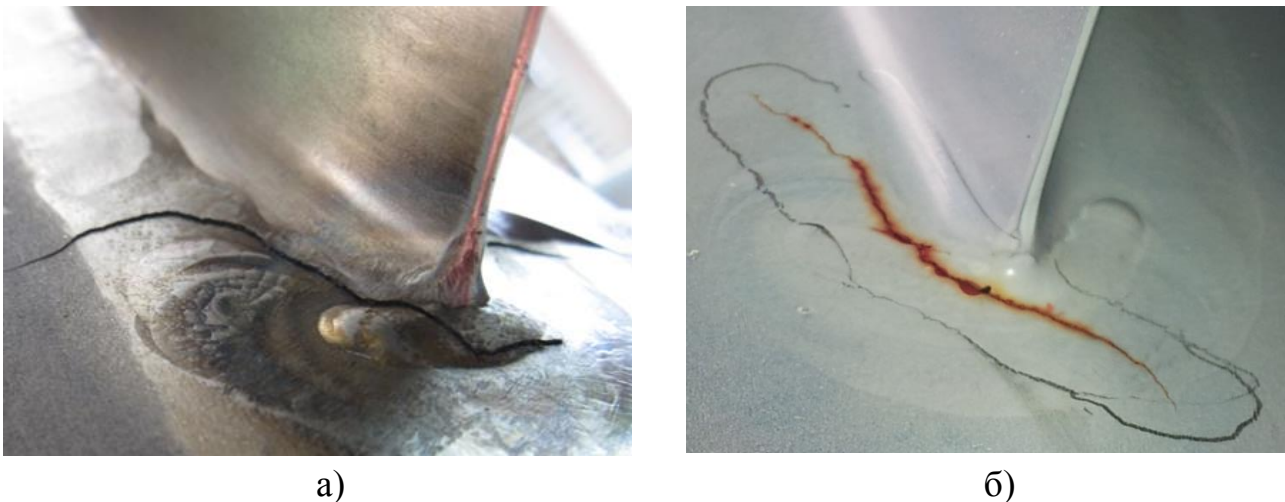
Тріщина вздовж зварного шва стійки і корпусу опори двигуна (вид із заду стійки).
